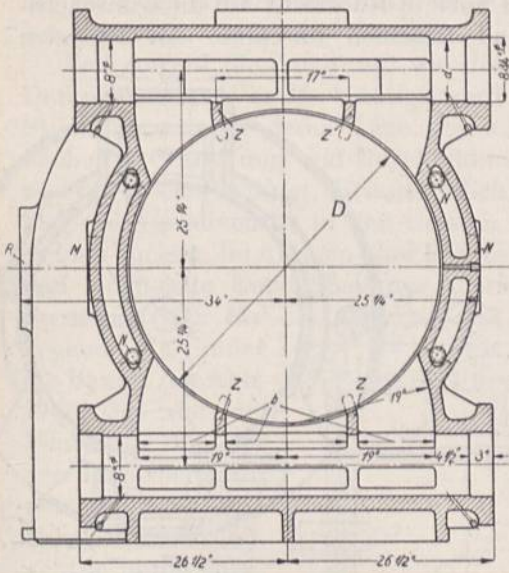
Zylinder mit Hahnsteuerung. Niederdruckzylinder der East-Jersey Wasserwerkmaschinen. Entwurf von Riedler und Stumpf. M. 1:25.
